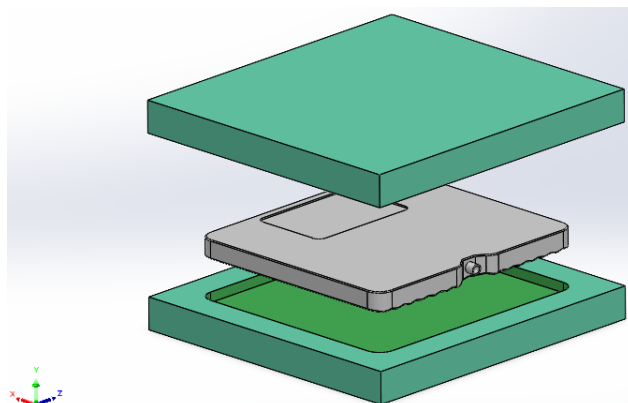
Vista explodida dos moldes de XPS e placa de HDPE de PCM (Solidworks).
